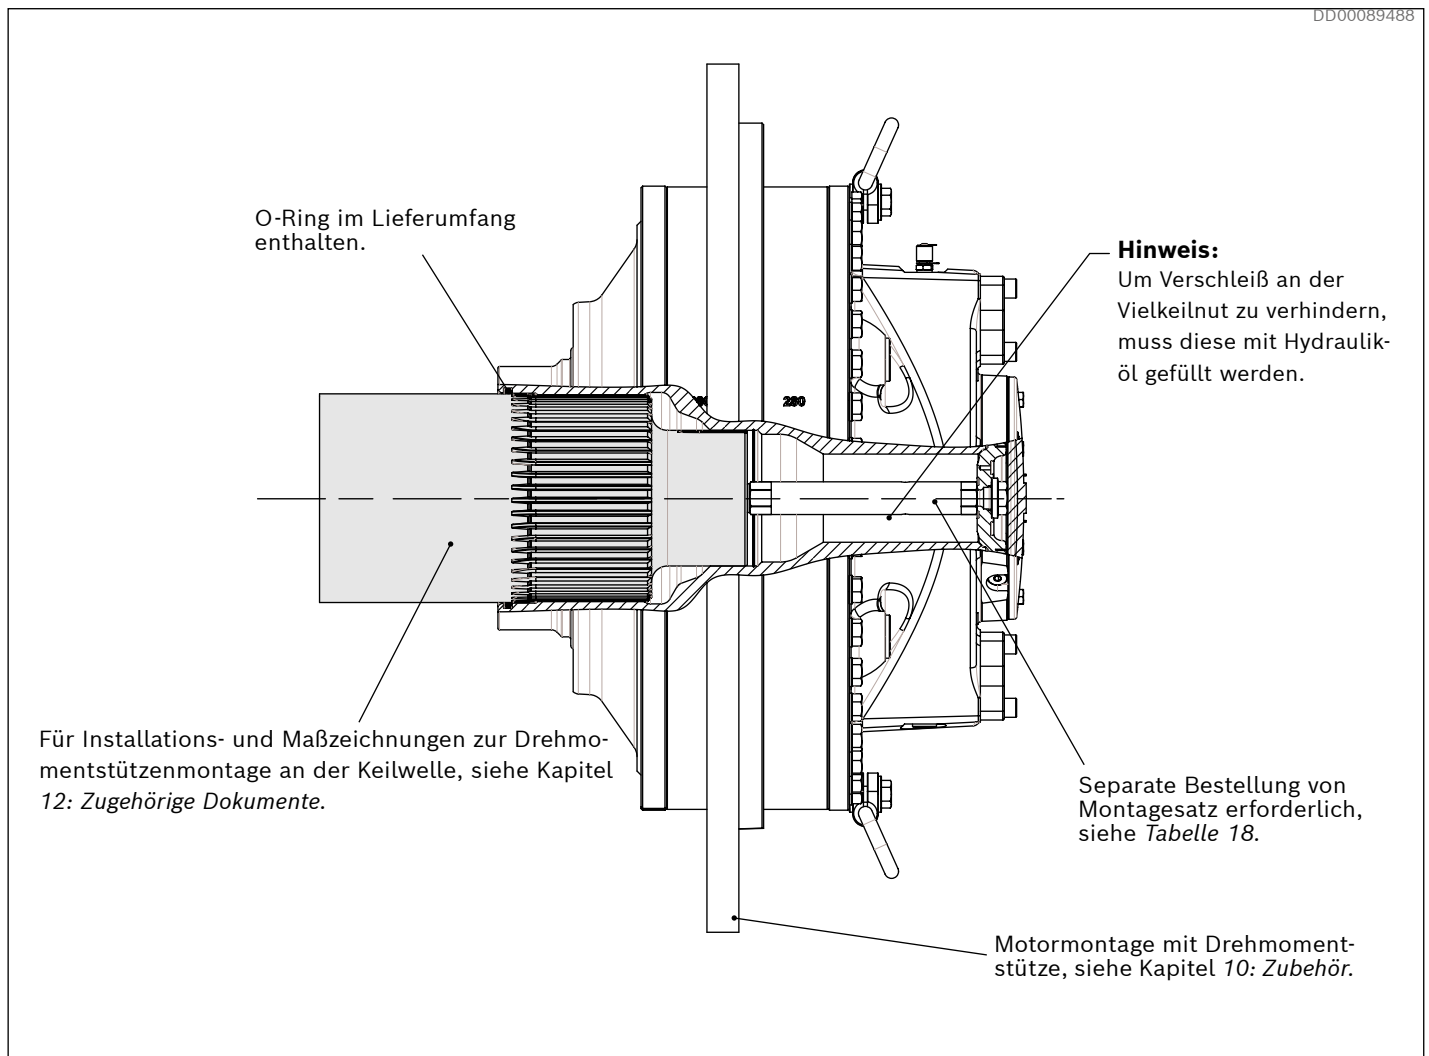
Motormontage mit Drehmomentstütze und Vielkeilnut
